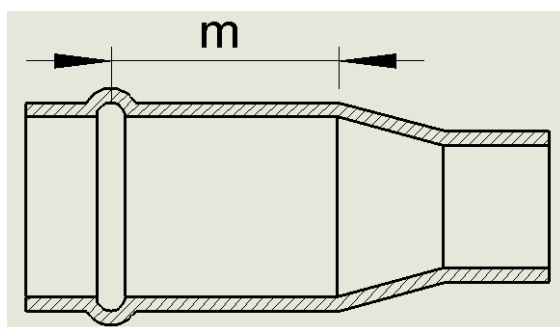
DIMENSIONES PARA SELLADO ELASTOMÉRICO (FUENTE: INEN 1331)
